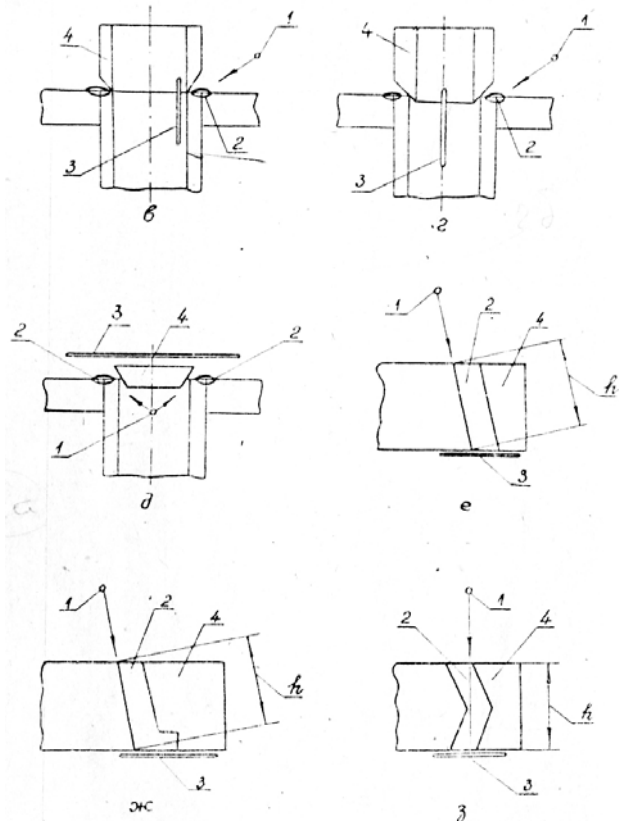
Схемы контроля сварных соединений труба - трубная доска.
